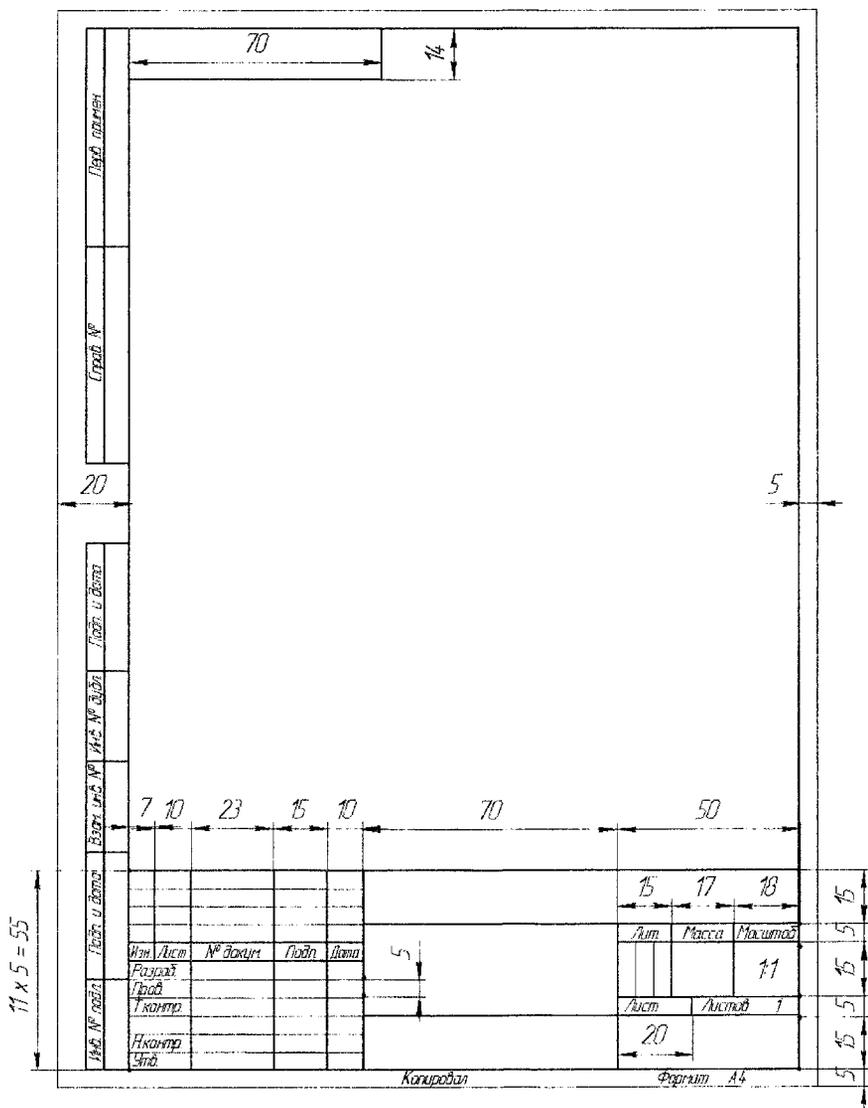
Основная надпись для чертежей и схем (по ГОСТ 2.104 – 68 ЕСКД)
